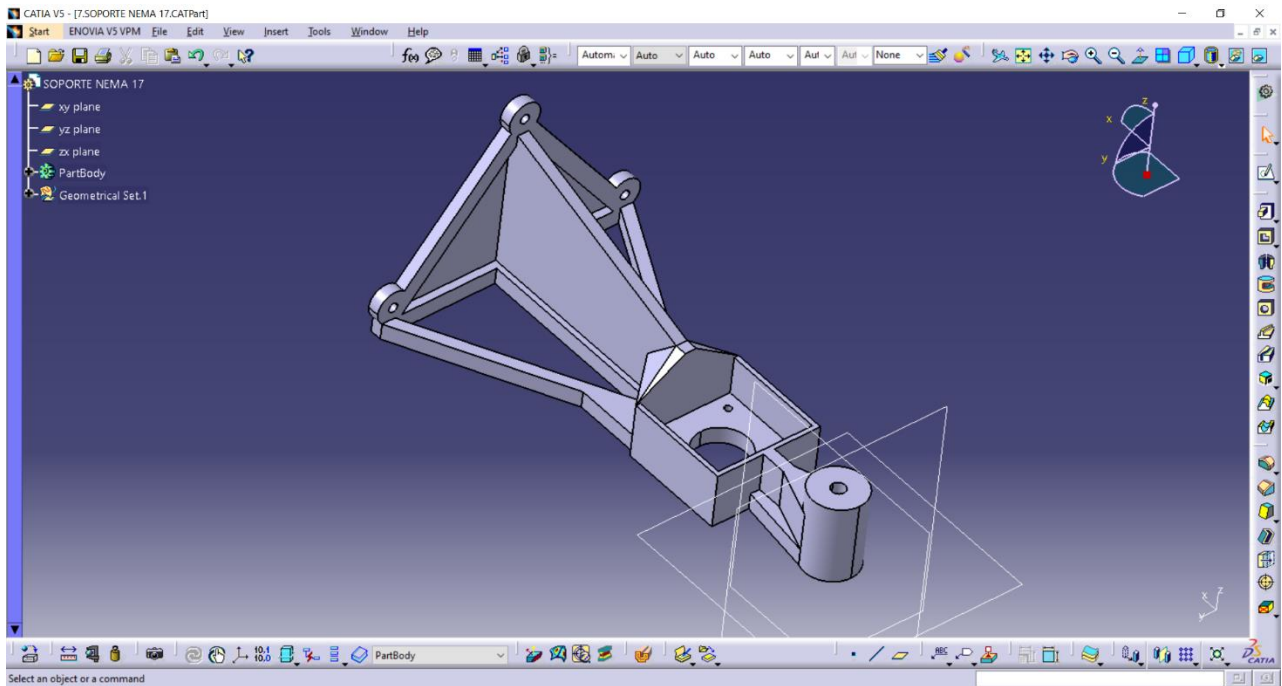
Componente estructural diseñado en Módulo Part Design
